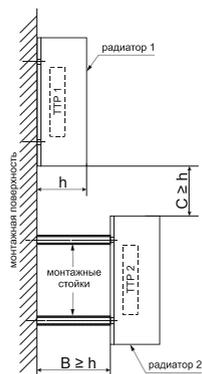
схема размещения ТТР при монтаже друг над другом
